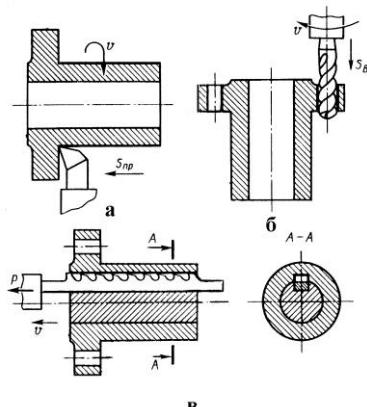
Схемы обработки поверхностей 1, 2, 3 детали:
